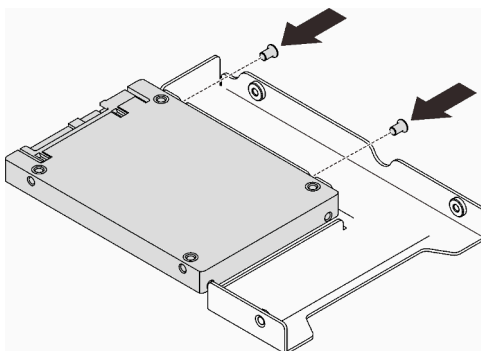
Anbringen der Schrauben, um das Laufwerk am Laufwerkadapter zu befestigen
